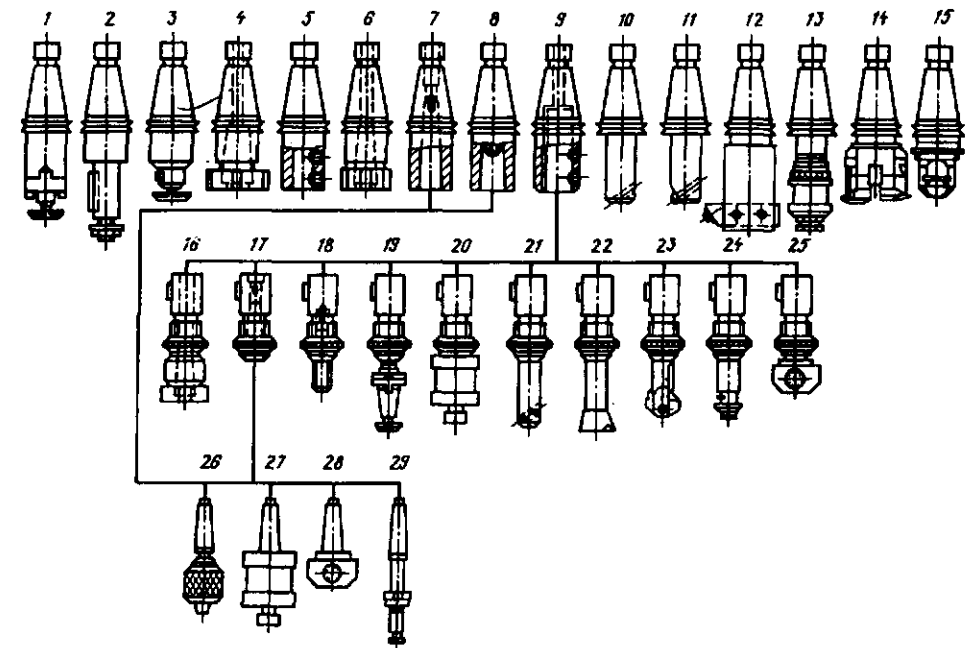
Подсистемы вспомогательного инструмента для станков с ЧПУ сверлильно-расточной и фрезерной группы: 1 – оправка с конусом 7 : 24 для насадных фрез с поперечной шпонкой; 2, 3 – оправки для насадных торцовых фрез с продольной шпонкой; 4 – патрон цанговый для закрепления инструмента диаметром 20 – 40 мм; 5 – втулки переходные для концевых фрез; 6 – патроны цанговые для закрепления инструмента с диаметром хвостовика 5 – 20 мм; 7 – втулки переходные для инструмента с конусом Морзе с лапкой; 8 – втулки переходные для инструмента с конусом Морзе с резьбовым отверстием; 9 – державки для регулируемых патронов, втулок и оправок; 10 – 12 – оправки расточные соответственно для получистового, чистового растачивания, для чистового растачивания сборные; 13 – оправки для подрезных пластин; 14 – головки расточные двухзубые; 15 – головки расточные универсальные; 16 – патроны цанговые регулируемые (диапазон зажима 2 – 25 мм); 17 – втулки регулируемые с внутренним конусом Морзе, универсальные; 18 – втулки регулируемые длинные с внутренним конусом Морзе; 19 – оправки регулируемые для насадных зенкеров и разверток; 20 – патроны регулируемые резьбонарезные; 21 – оправки регулируемые для получистового растачивания; 22 – оправки регулируемые расточные двухзубые; 23 – оправки регулируемые для крепления пластин перовых сверл; 24 – оправки регулируемые для дисковых фрез; 25 – патроны регулируемые; 26 – патрон с конусом Морзе сверлильный трехлапчатый без ключа; 27 – патроны с конусом Морзе резьбонарезные; 28 – патроны с конусом Морзе расточные; 29 – оправки с конусом Морзе для насадных зенкеров и разверток
